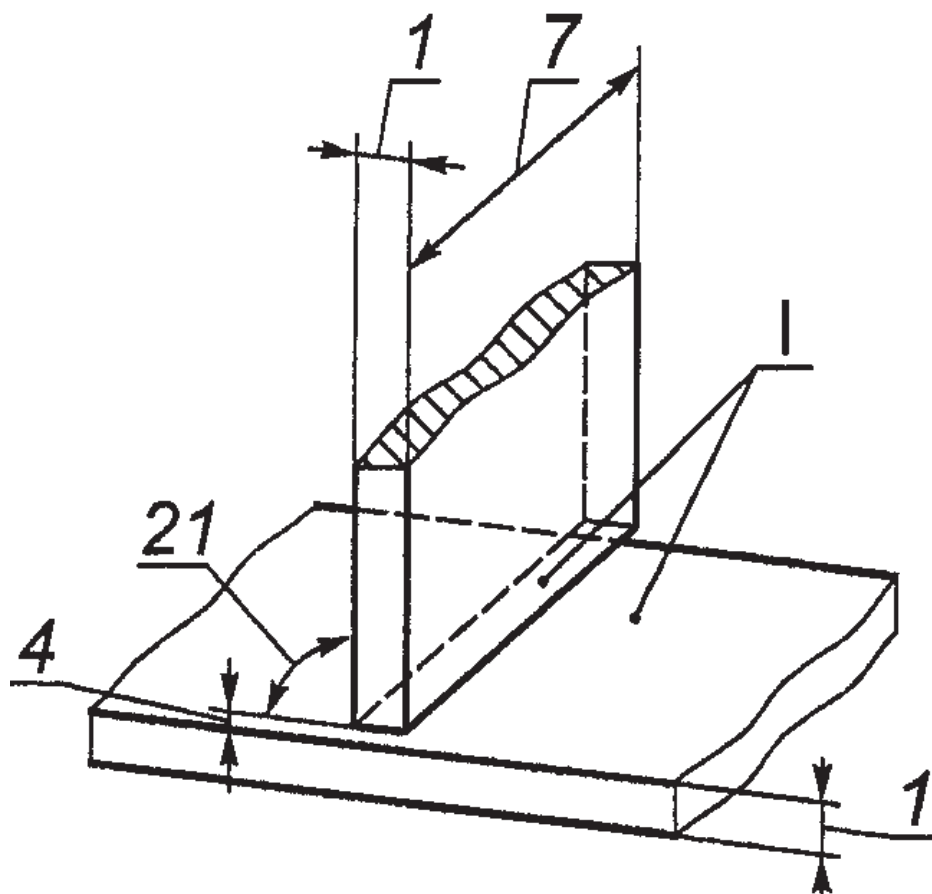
Подготовка под сварку таврового соединения Figure 6. Preparation for fillet weld (T-joint) Figure 6. pour soudures d'angle sur assemblage en T
